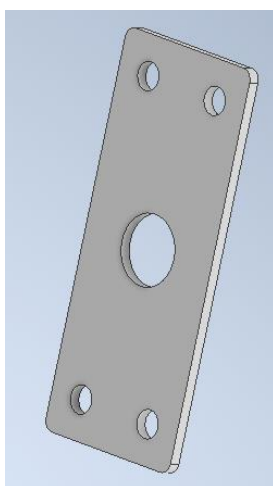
Zamontowane zabezpieczenie wlotu powietrza (opracowanie własne)
